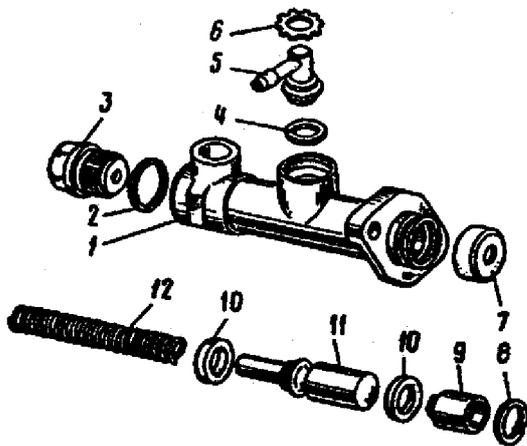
Componentes do cilindro mestre: 1 - corpo; 2 - arruela de retenção; 3 - tampa; 4 - junta; 5 - tubo de alimentação; 6 - arruela de retenção; 7 - coifa; 8 - anel de retenção; 9 - êmbolo da haste; 10 - gaxeta; 11 - êmbolo do cilindro principal; 12 - mola.
